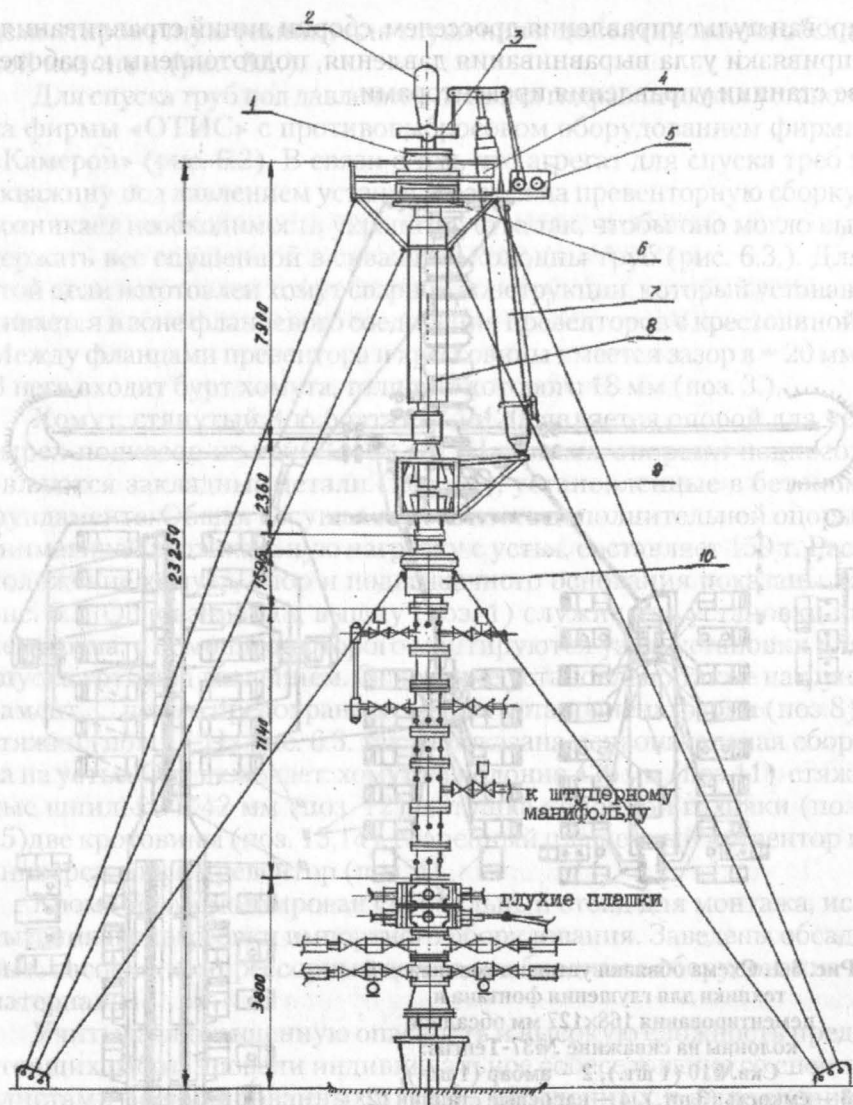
Схема установки для спуска труб в скважину под давлением: 1 – ключ; 2 – вертлюг; 3 – подвеска; 4 – рабочая площадка; 5 – противовес лебедки; 6 – подвижный захват; 7 – стрела; 8 – домкрат; 9 – неподвижный захват; 10 – универсальный пренватор 11”
